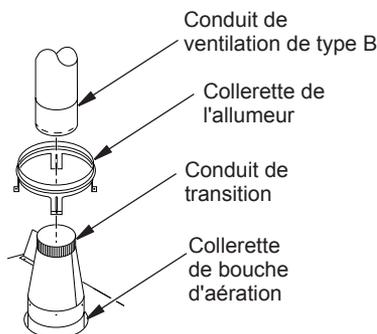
Installation du conduit de transition et de la collerette de l'allumeur
